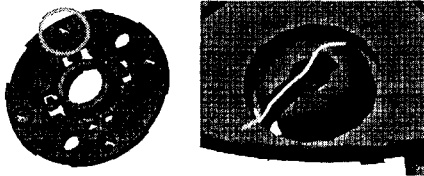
Weld line에 의해 문제가 되고 있는 부분 (○) 와 Weld line에 의한 파괴 예상선
